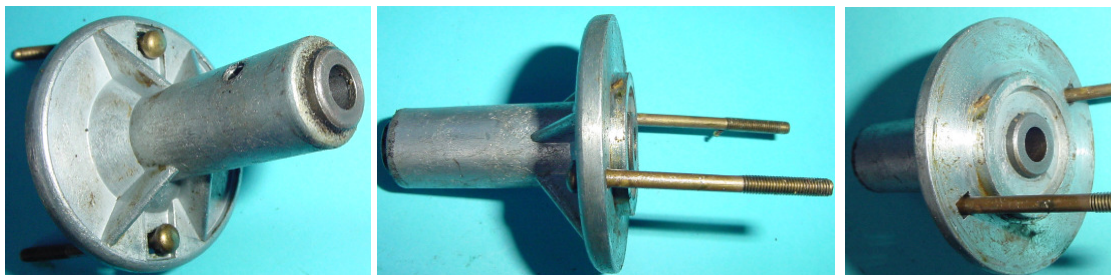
Innerer Lagerhals mit den verdeckten Gewindebolzen
